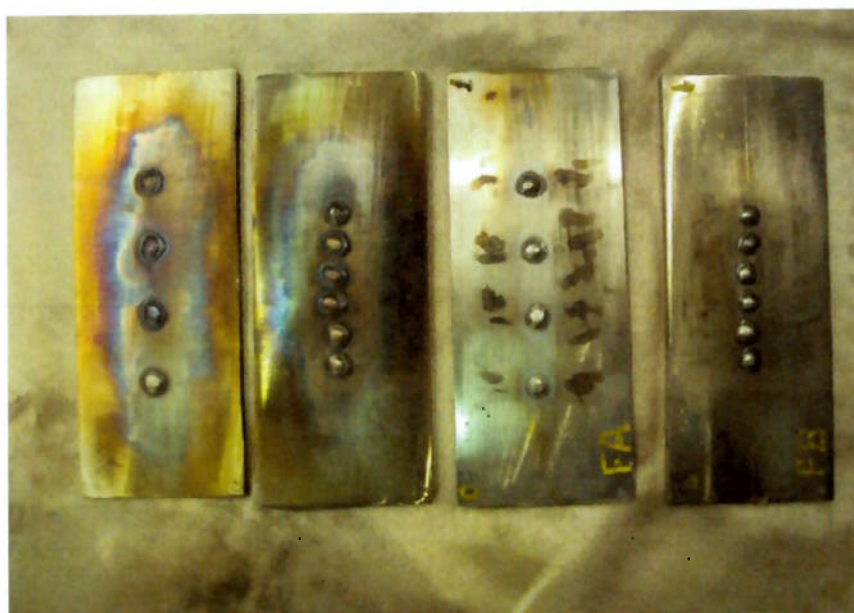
Corpo de Prova soldado espessura de 10 mm
